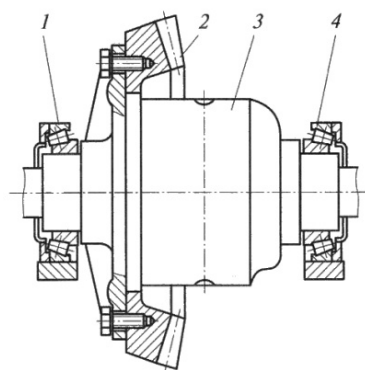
Установка ведомой шестерни конической главной передачи: 1, 4 — подшипники; 3 — ведомая шестерня; 3 — дифференциал
